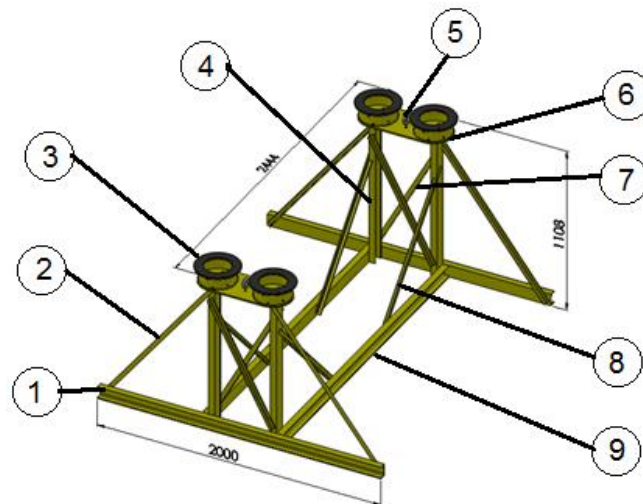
Estrutura de suporte final do Conjunto Travessa de Carga/Travessa Dançante
